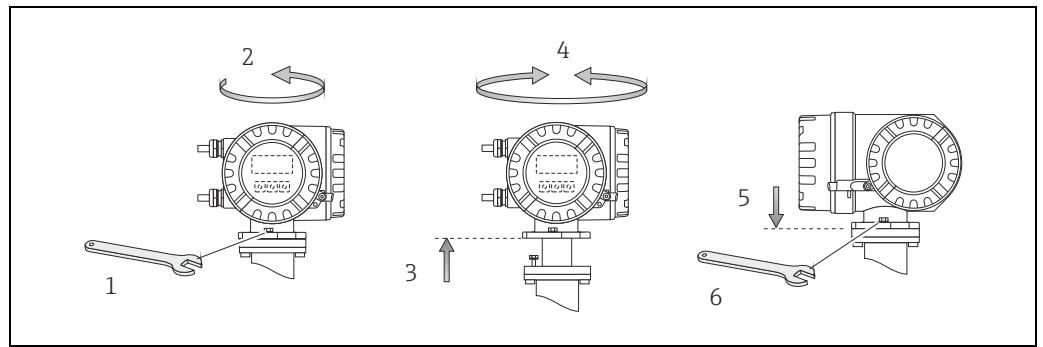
Rotación de la caja del transmisor (caja de aluminio para montaje en campo)
